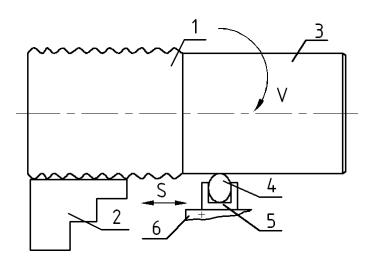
Схема пластического деформирования поверхностного слоя для уменьшения шероховатости:
